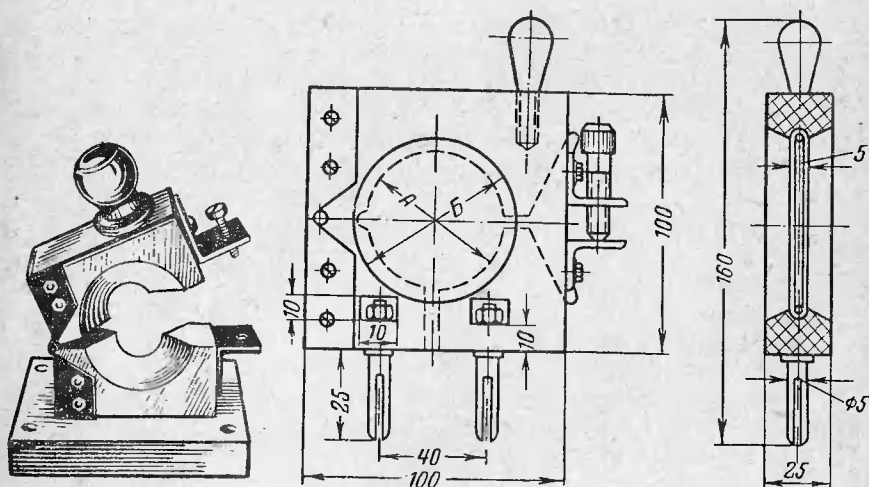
Приспособление для резки труб местным нагревом (глубина канавки для укладки нагревателя равна половине диаметра проволоки).
